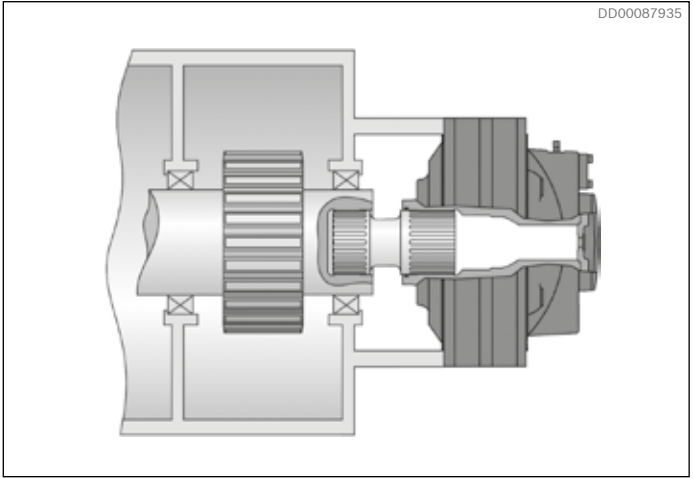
Flanschmotor mit Vielkeilnut zur Vermeidung hoher Radialbelastung von der Abtriebswelle.
